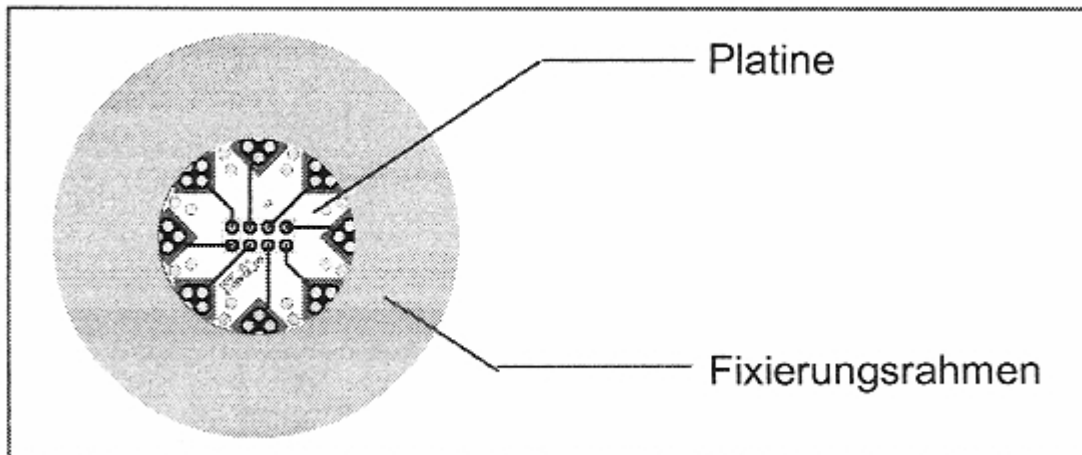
Mechanische Fixierung der Platine auf Fixierungsrahmen
